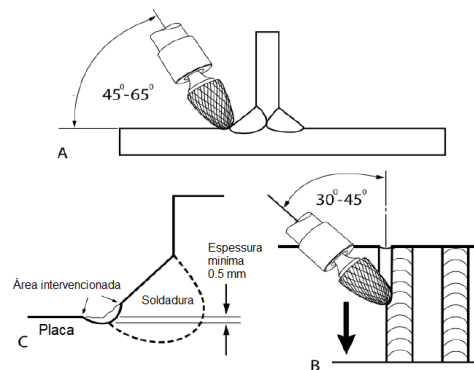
Técnica de moagem do pé da soldadura, adaptado de [15]
